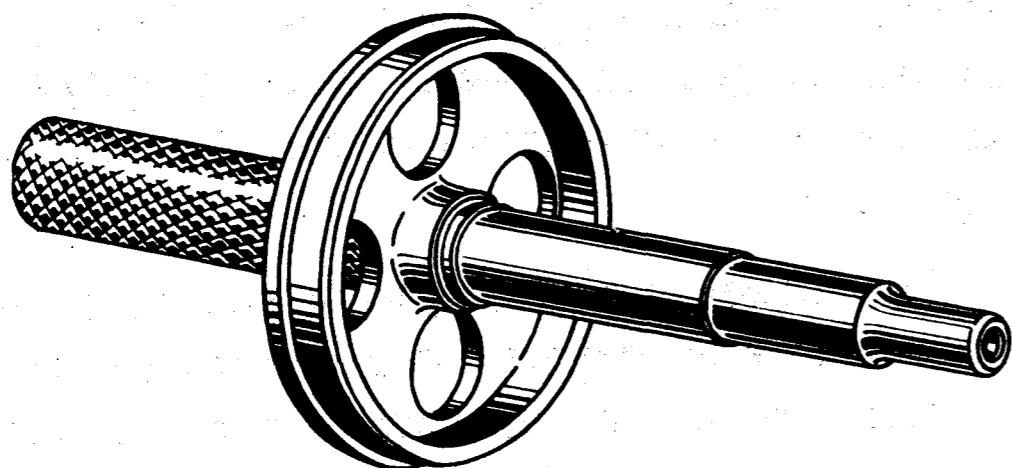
Оправка 7820-5046 для установки ведомого диска
